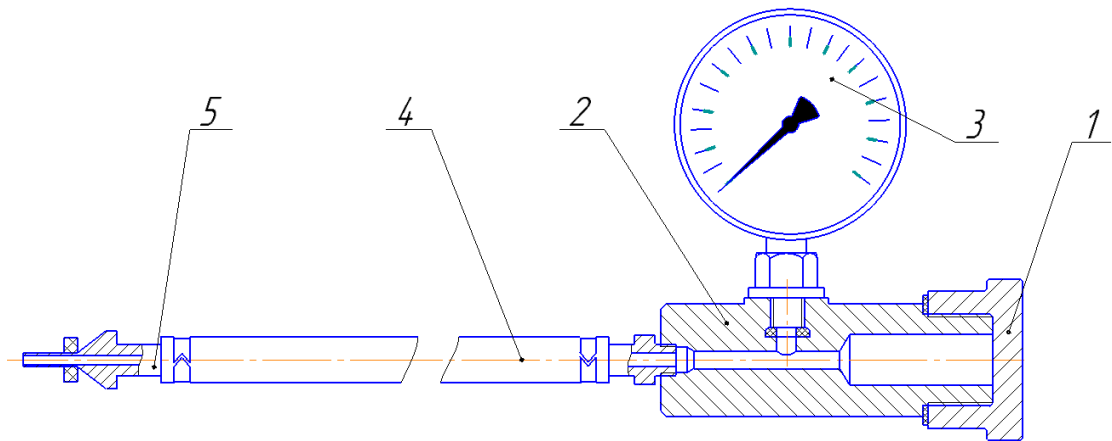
Прилад для контролю рівня вакууму: 1 – корпус; 2 – кришка; 3 – вакууметр; 4 – гумовий шланг; 5 - наконечник.
